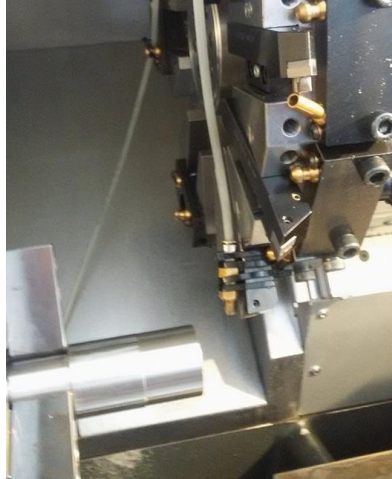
9 Sujeción de la boquilla en el punto de ataque
